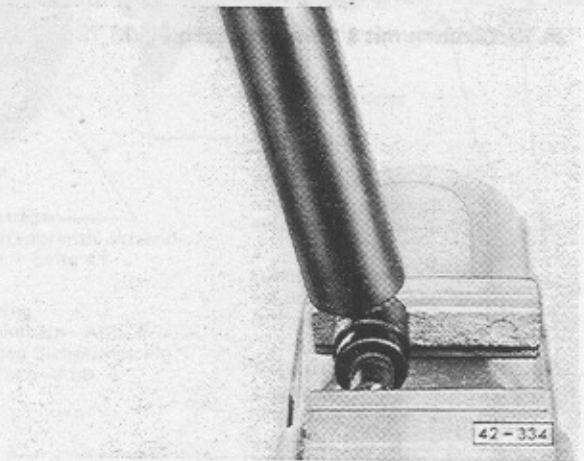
Gummilager und Buchse für Stoßdämpfer einpressen
